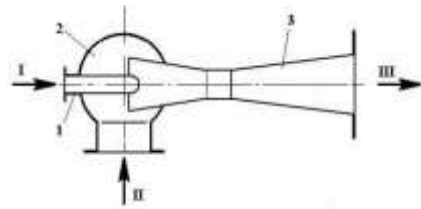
Струминний насос: I – робоча рідина; II – переміщувана рідина; III – суміш. 1 – сопло; 2 – камера змішування; 3 – дифузор
